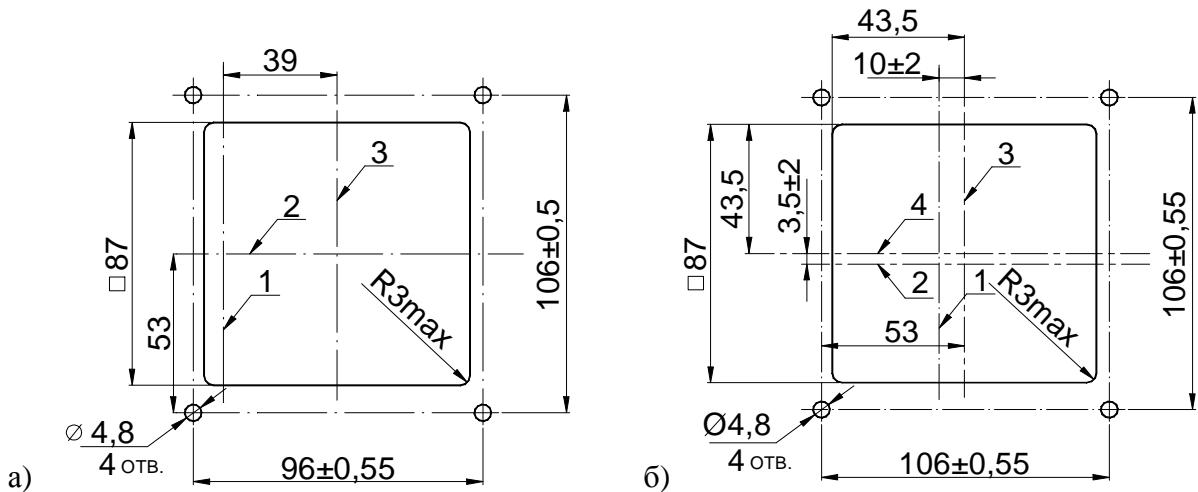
Расположение отверстий для крепления ручного дистанционного привода
